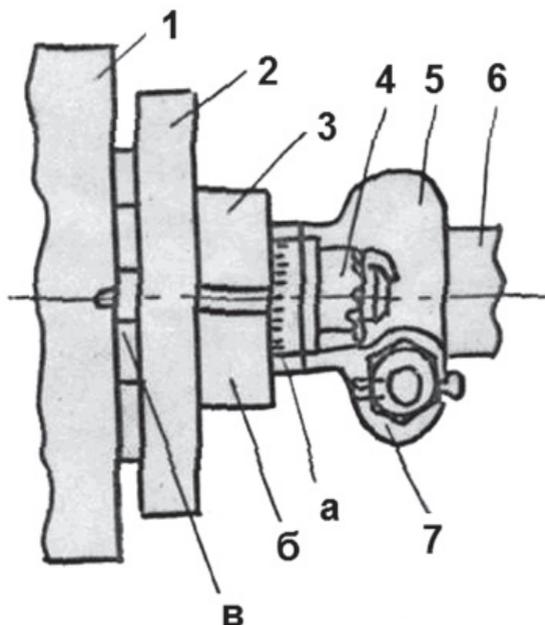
Установочные метки для регулировки угла опережения впрыска топлива на двигателе ЯМЗ–240Б:
